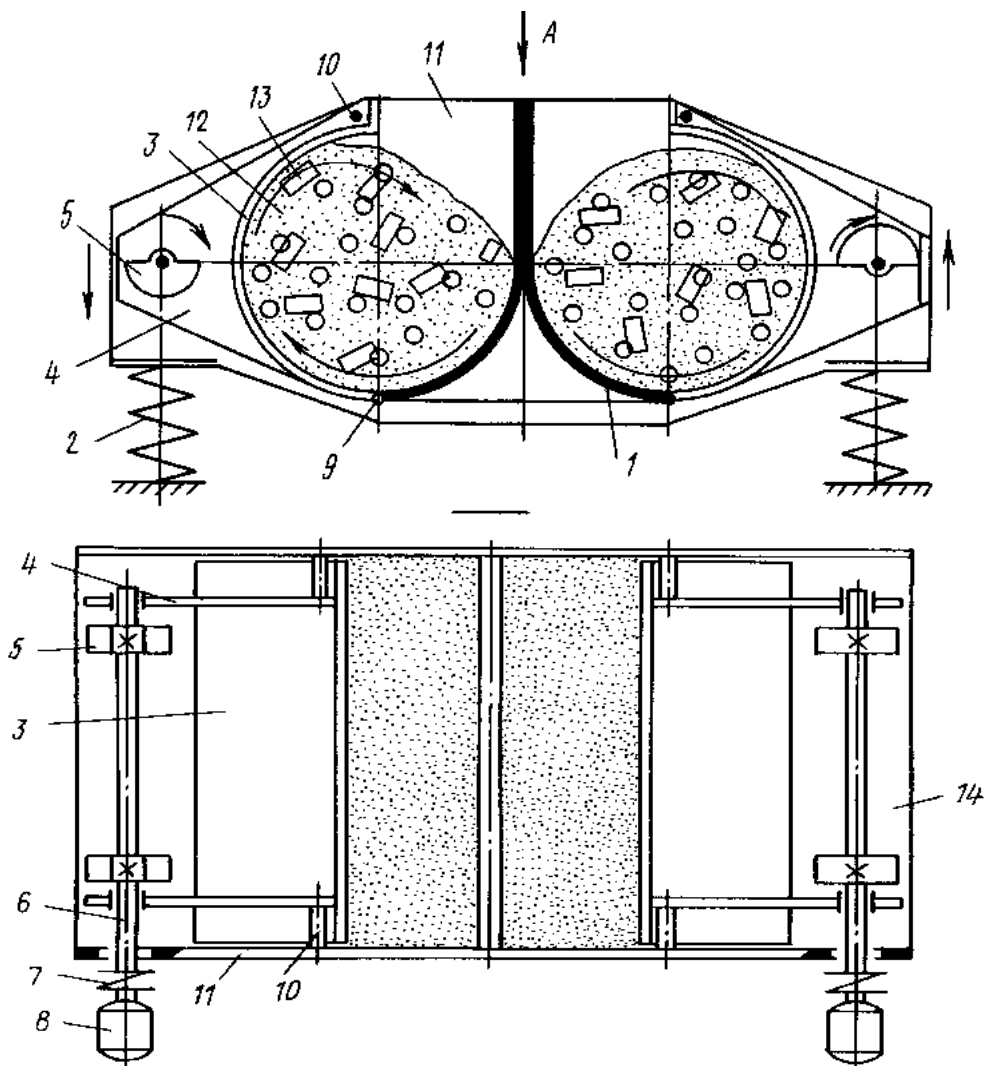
Вібраційна машина з пружними елементами: 1 – пружний робочий орган; 2 – пружинна підвіска; 3 – бокова стінка; 4 – ребра; 5 – вібробудувач; 6 – вал; 7 – еластична муфта; 8 – двигун; 9 – осі; 10 – стержневі пружини; 11 – торцева стінка; 12 – оброблюване середовище; 13 – деталі; 14 – платформа
